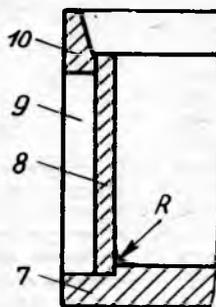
Соединение деталей формы в сварном варианте
